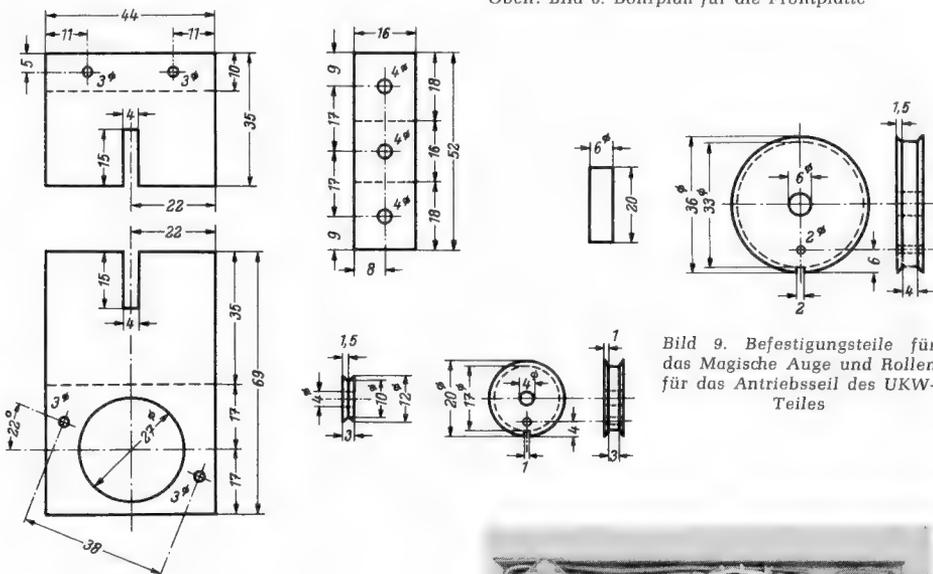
Befestigungsteile für das Magische Auge und Rollen für das Antriebsseil des UKW-Teiles
